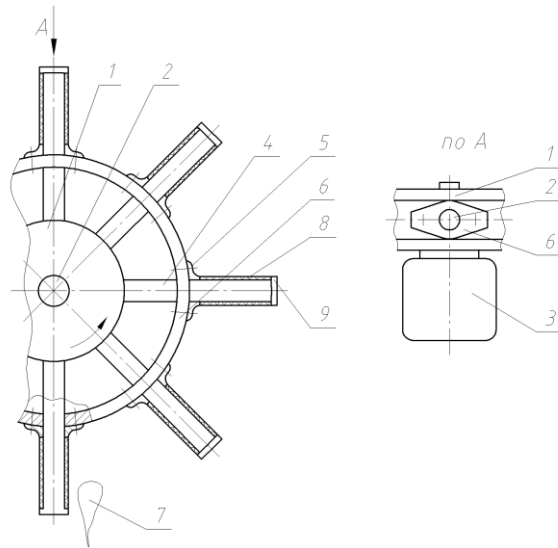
Загальний вигляд роторного очисника навісної трьохрядної коренезбиральної машини: 1 – маточина; 2 – отвір привідного валу; 3 – редуктор; 4 – маточини; 5 – кронштейни; 6 – диск жорсткості; 7 – коренеплоди; 8 – еластичні трубки; 9 – упори еластичних трубок.
